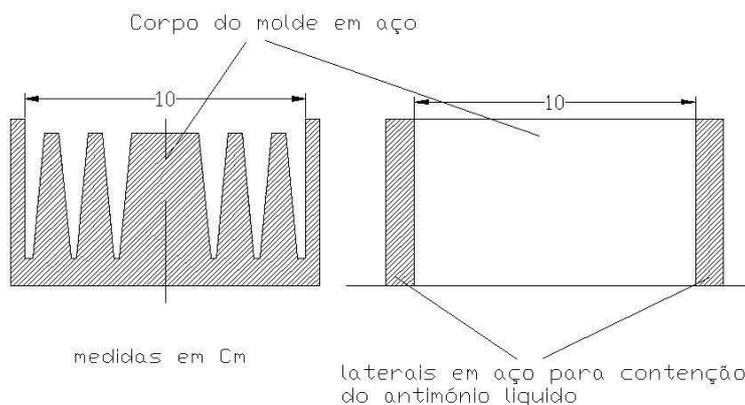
Molde em aço para fabrico do dissipador de calor em antimónio
